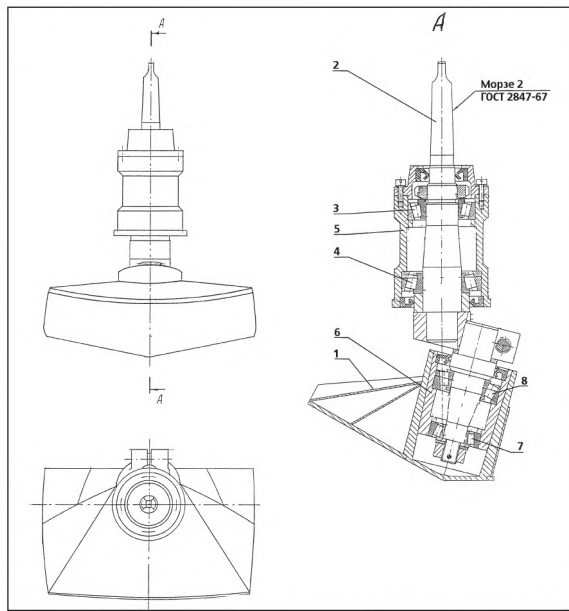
Устройство нагнетателя. 1 - рабочий орган, 2 - вал, 3, 4, 7, 8 - подшипники, 5 - ступица, 6 - коническая втулка.
